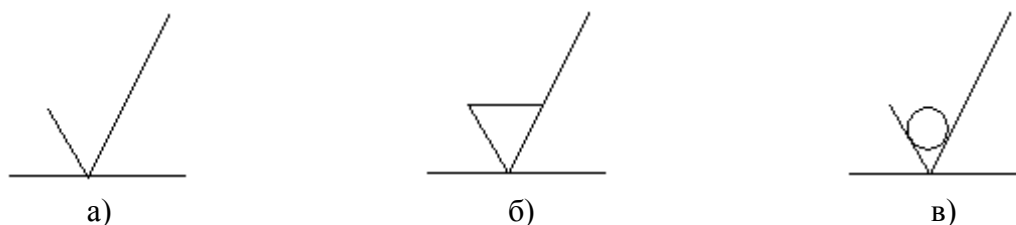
Знаки обозначения шероховатости поверхности (а, б, в).
